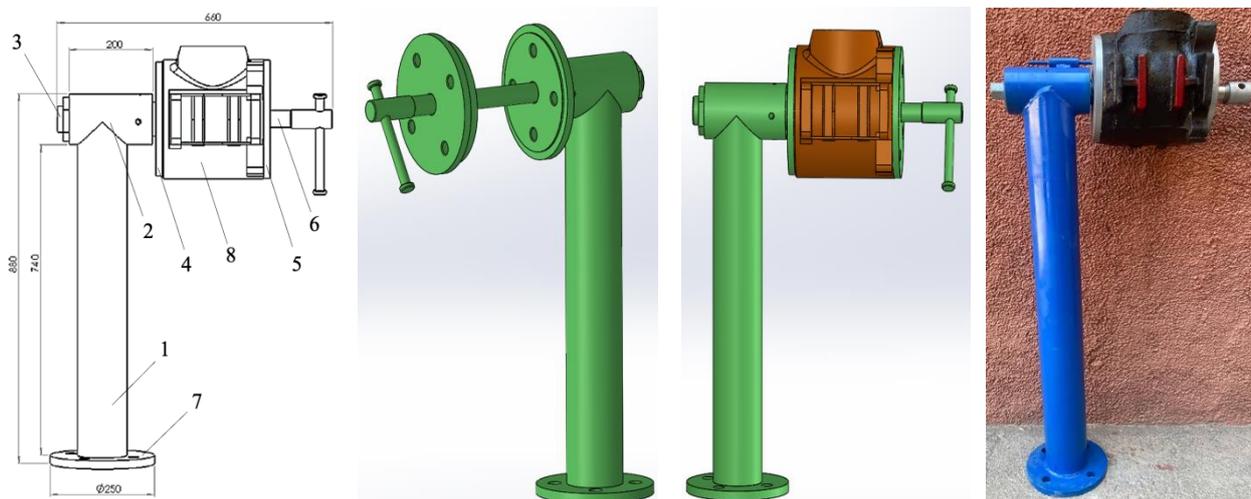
Общий вид устройства для наплавки корпусов букс:
